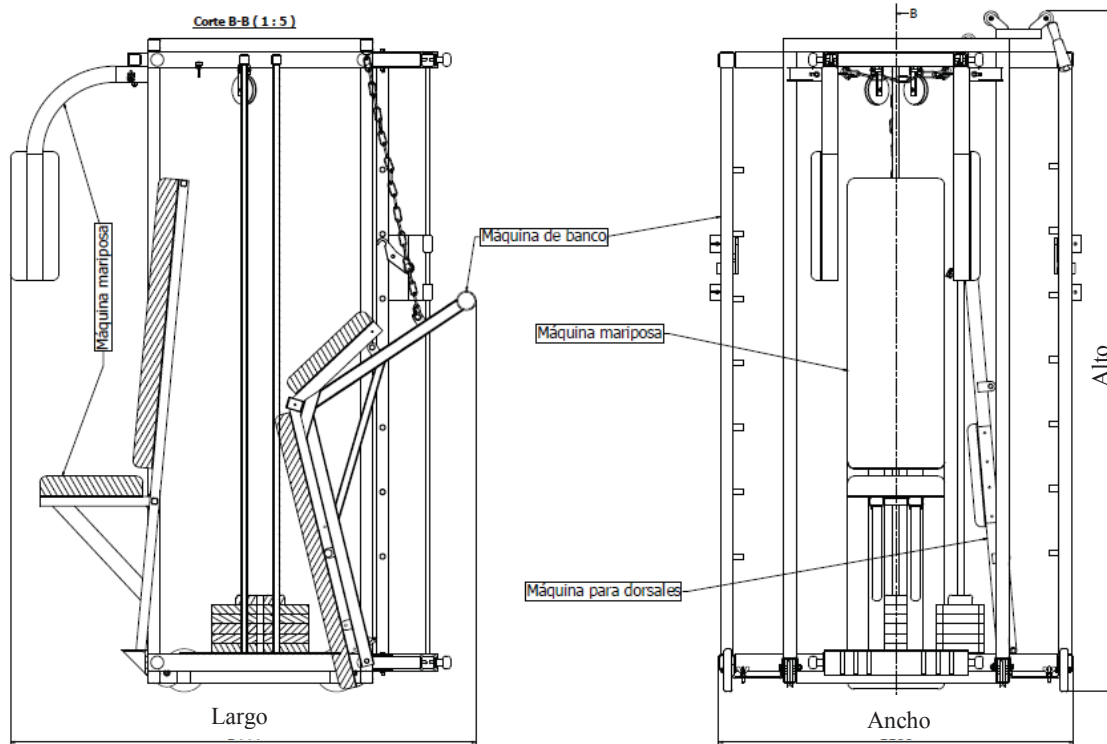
Dimensiones en la posición de transporte de la máquina de tren superior.
